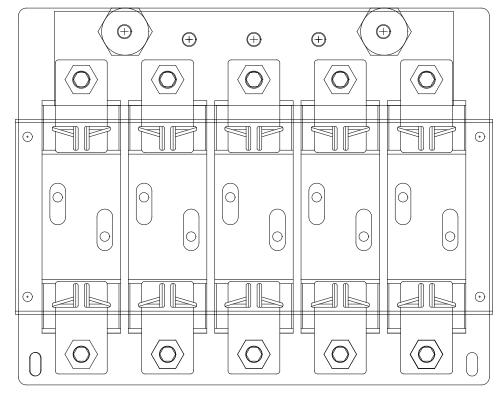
Allacciamento cavi in arrivo dalle String Box: vista frontale
